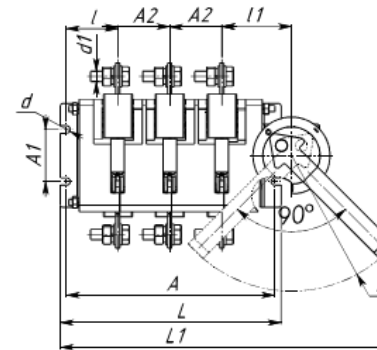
Б Выключатель-разъединитель на одно направление 3-полюсный с передней поворотной рукояткой
